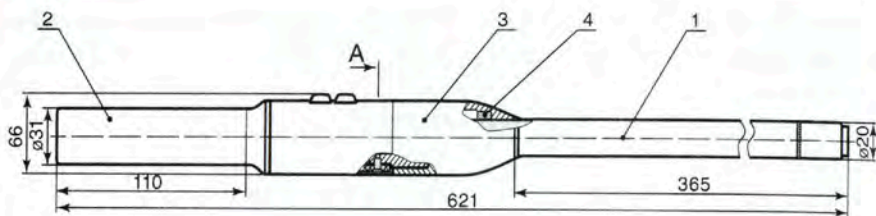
Чертеж общего вида эндоскопического тактильного прибора
